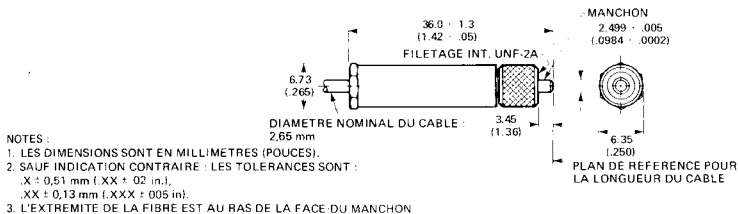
Dimensions de montage, en millimètres (pouces)
